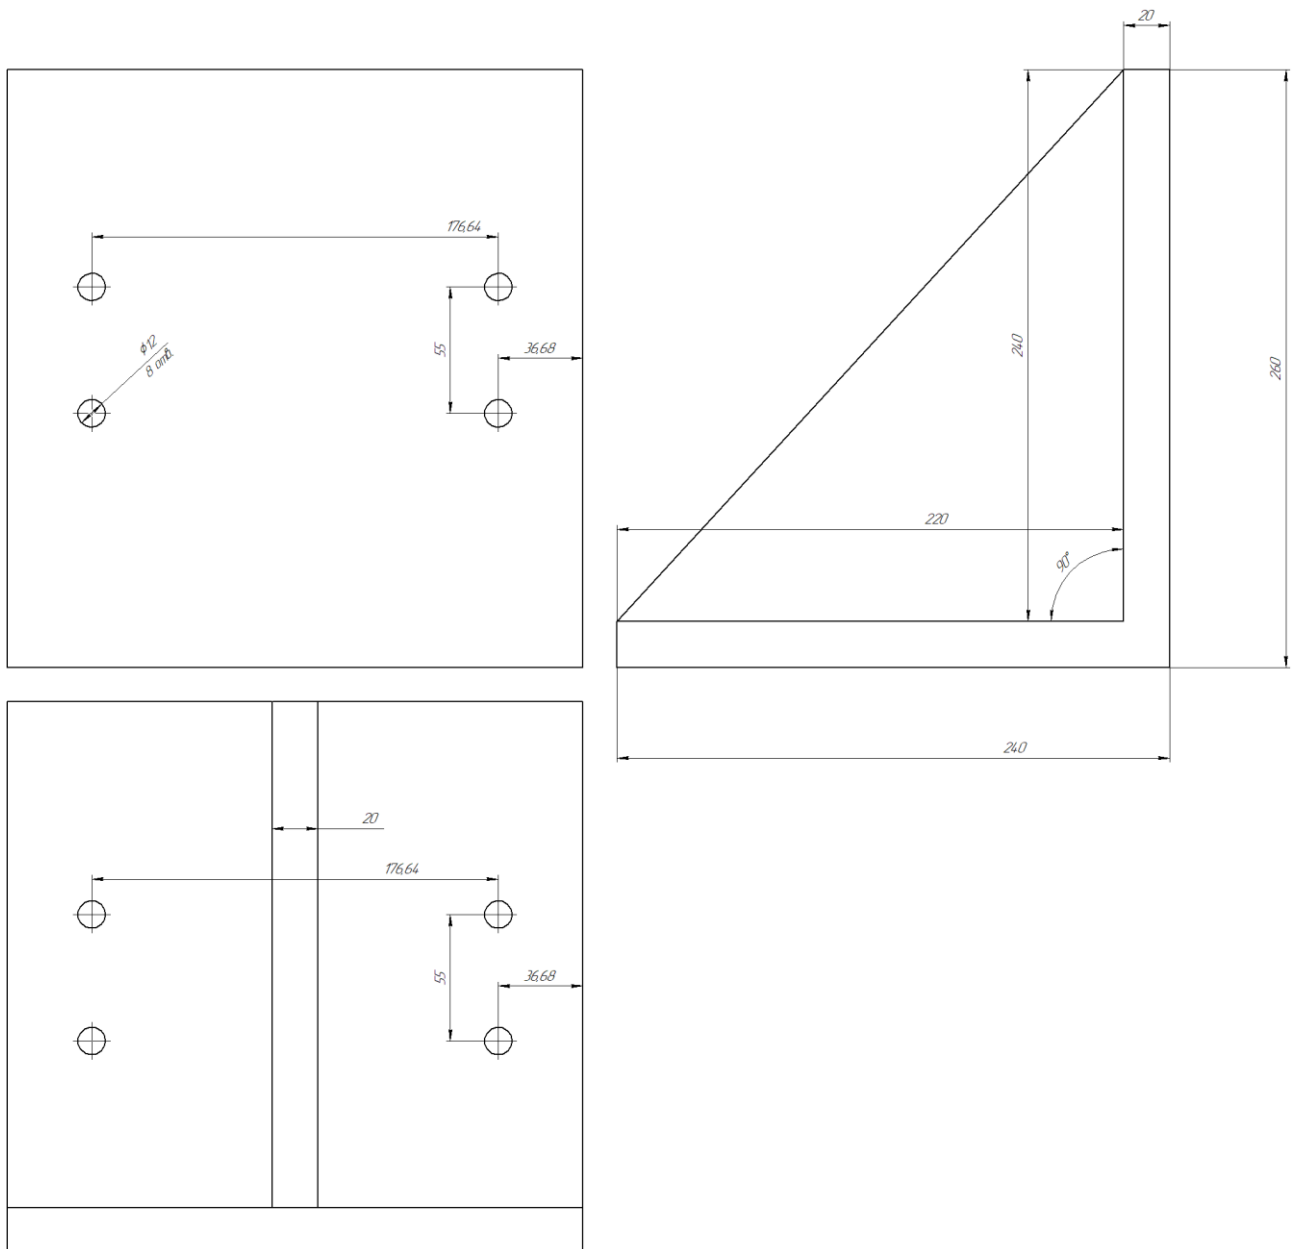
Ескіз перехідника для встановлення фрезерної приставки
